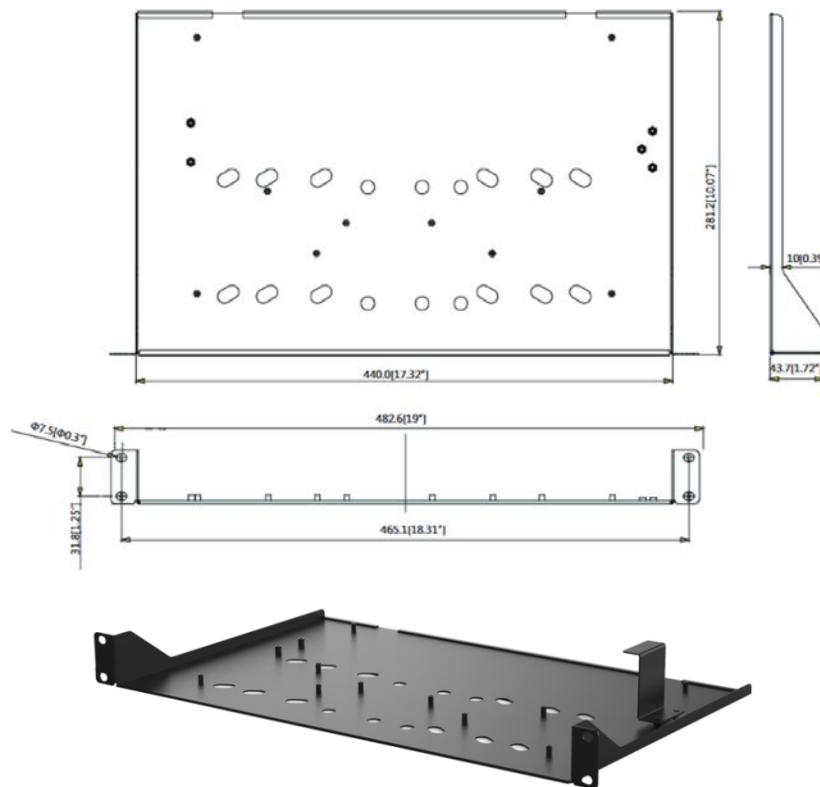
Внешний вид и габариты BOLID BR-111
